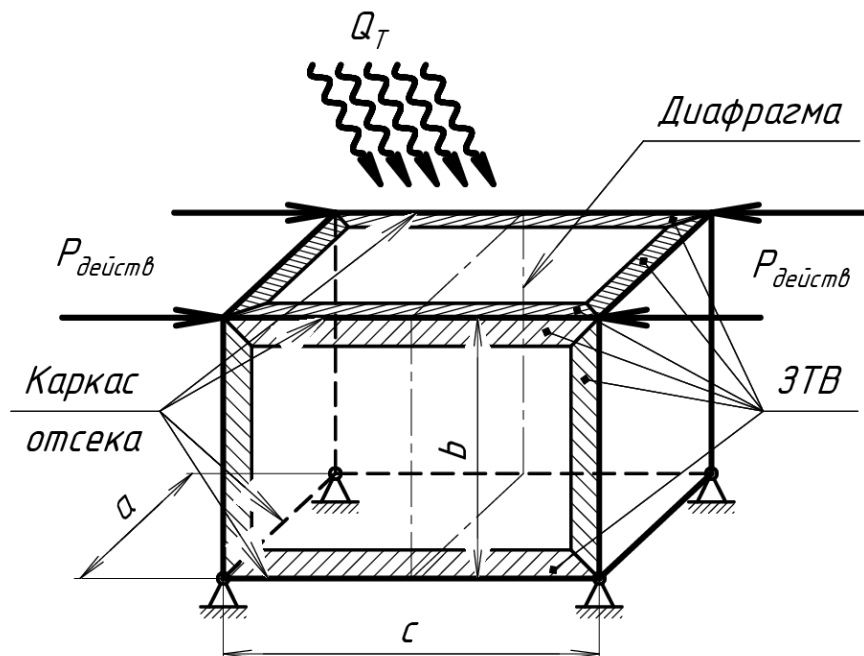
Схема обобщенного сварного отсека, нагруженного действующими термомеханическими усилиями.
